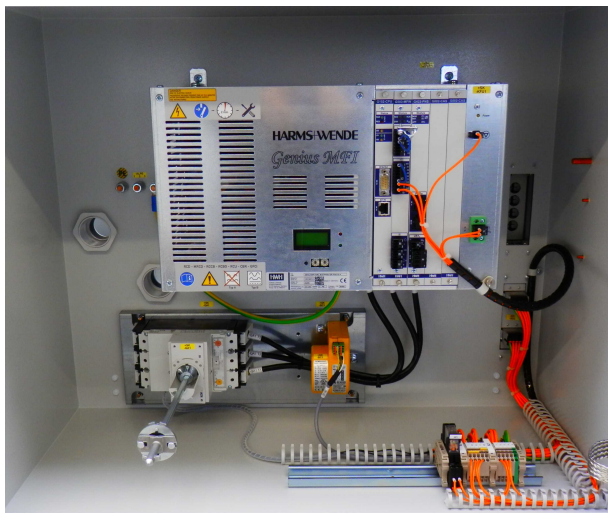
Roboter aufsatzschrank Innenansicht
